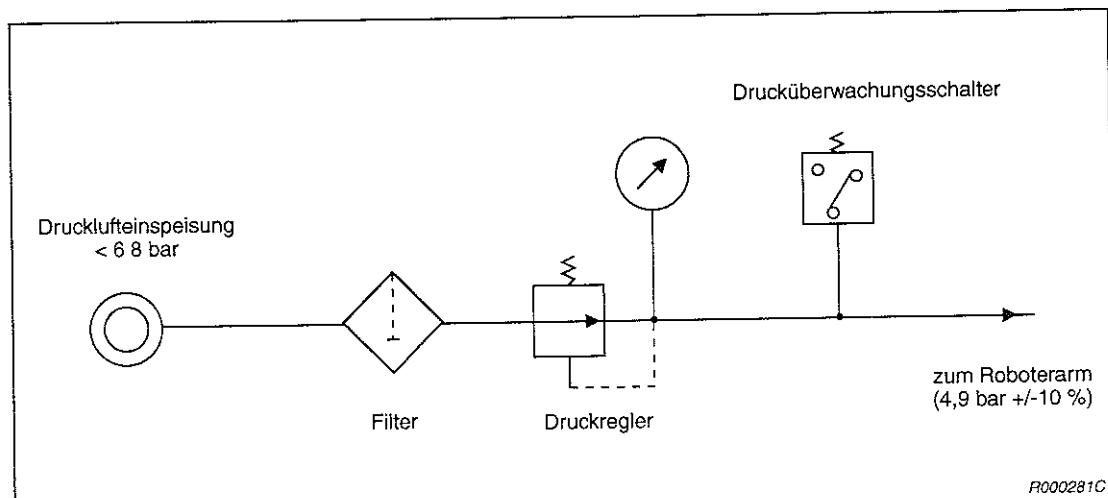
Beispielschaltung der Pneumatikversorgung für die Greifhand
